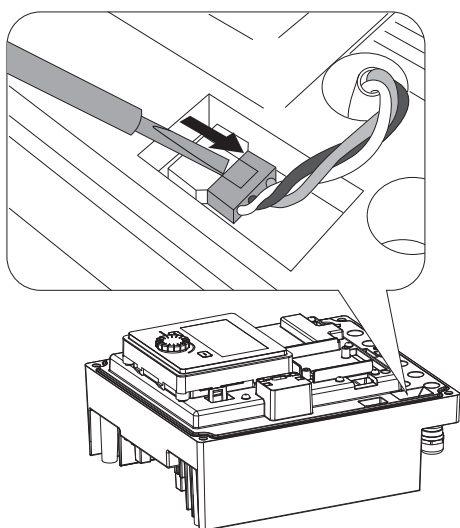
Zdjąć kabel zasilający wentylatora modułu
